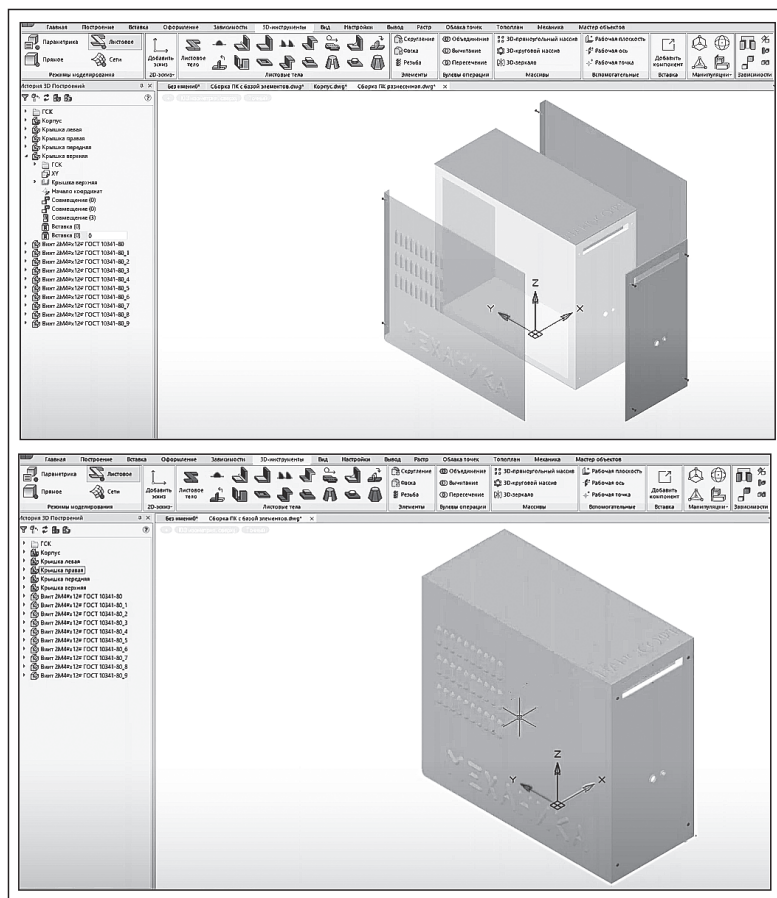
Сборка 3D-модели изделия «Корпус компьютера»
